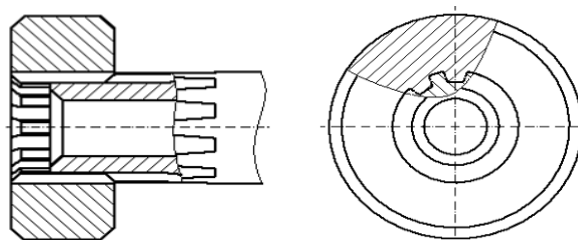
Фрагмент кресленника шліцьового з'єднання в пакеті Autodesk Inventor
